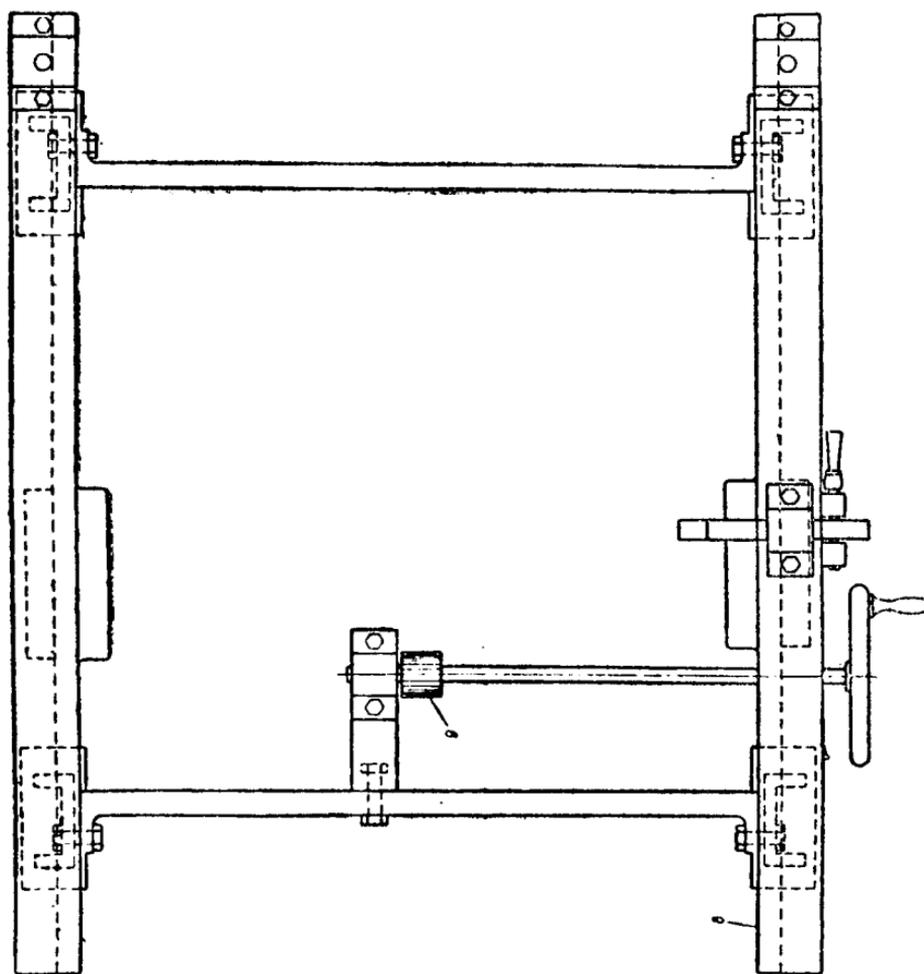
Проект станка т. Пурецкого—вид сверху; 8—место, откуда вставляется приспособление с зажатыми планками, 9—шестерня, сцепляющаяся с рейкой приспособления.
